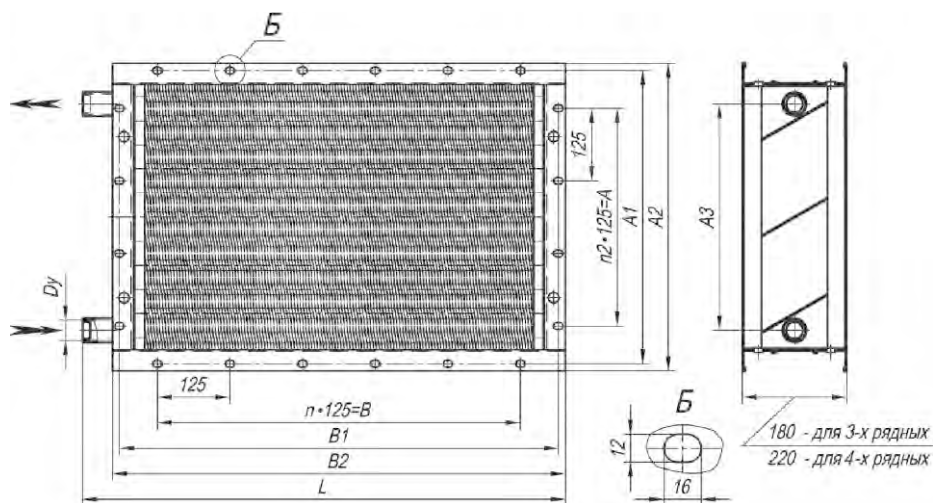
Габаритные и присоединительные размеры воздухонагревателей типа ВНВ.
